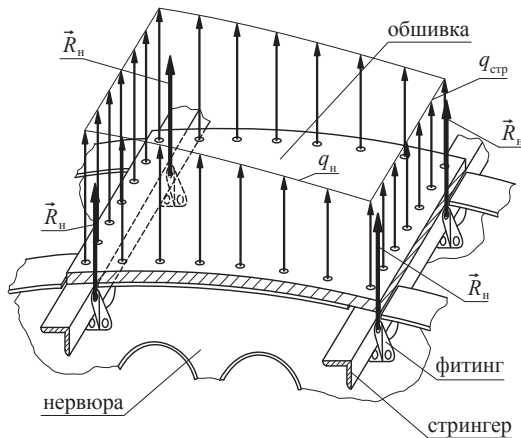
Схема нагружения обшивки, стрингеров и нервюр аэродинамической нагрузкой
